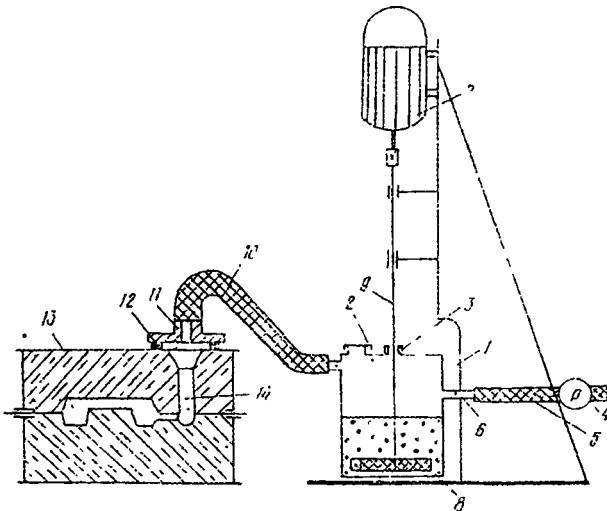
Схема устройства для приготовления и нанесения активированного покрытия на рабочую поверхность литейной формы
